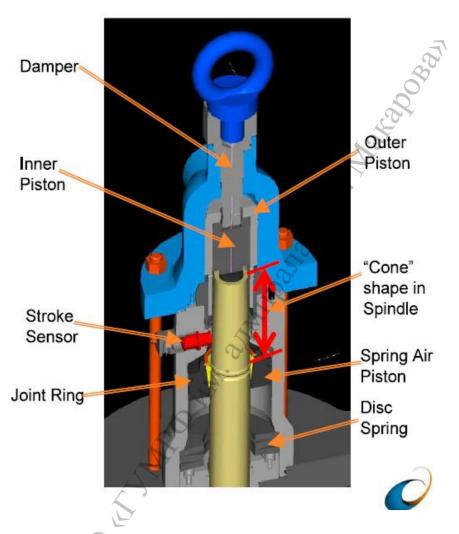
Exhaust valve (EV) - Выпускной клапан: Damper – Компенсатор, Inner piston (IP) – «Открывающее положение» поршня, Stroke sensor (SS) - Датчик хода, Joint ring (JR) - Присоединительная пружина, Outer piston (OP) – «Закрывающее положение» поршня, Sprint air piston - «Воздушная пружина», Disc spring - Дисковая пружина
